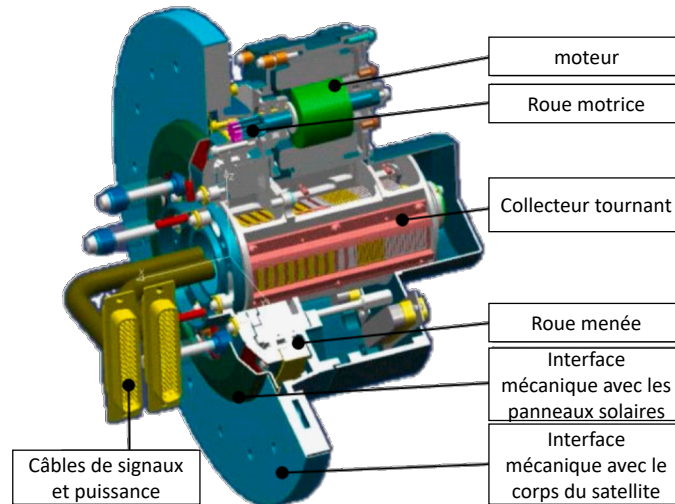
Composition du Solar Array Drive Assembly (SADA)
